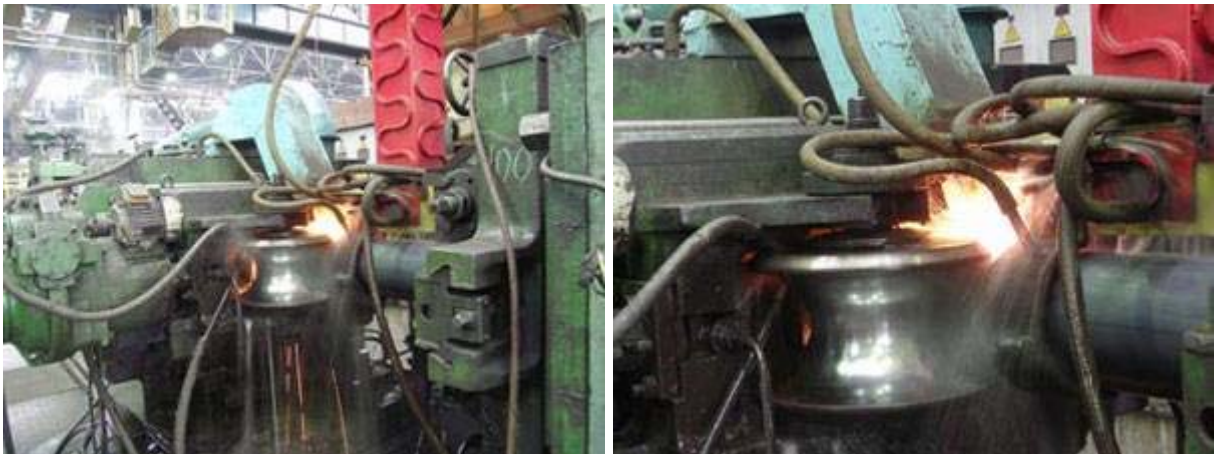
Трубозварювальне устаткування для подовжнього шва
